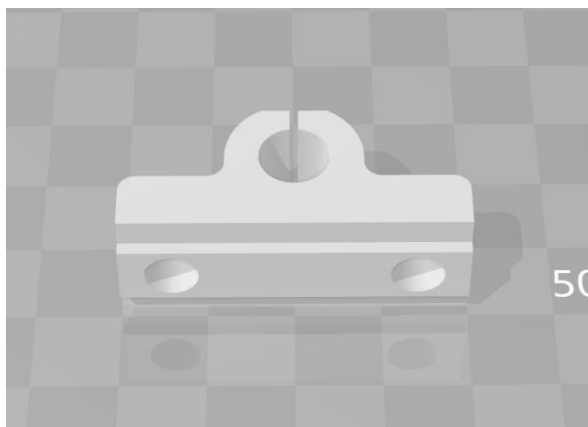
Držák řemenice (1) – Autor: Rebel RepRap
